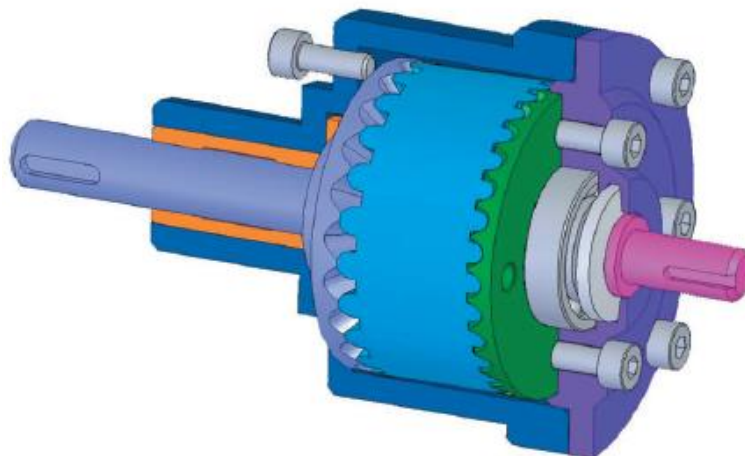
Сборка волнового торцевого кинематического редуктора
